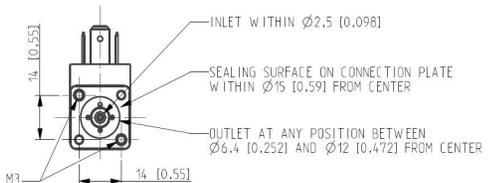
Dimensiones de montaje en pedestal, ancho de bobina de 20 mm
